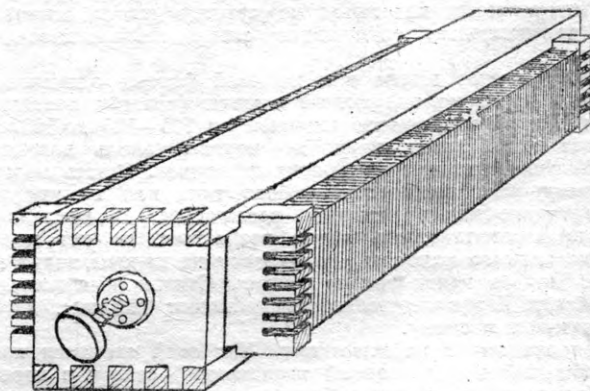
Двусторонний шаблон для фрезерования зубьев пластинок
